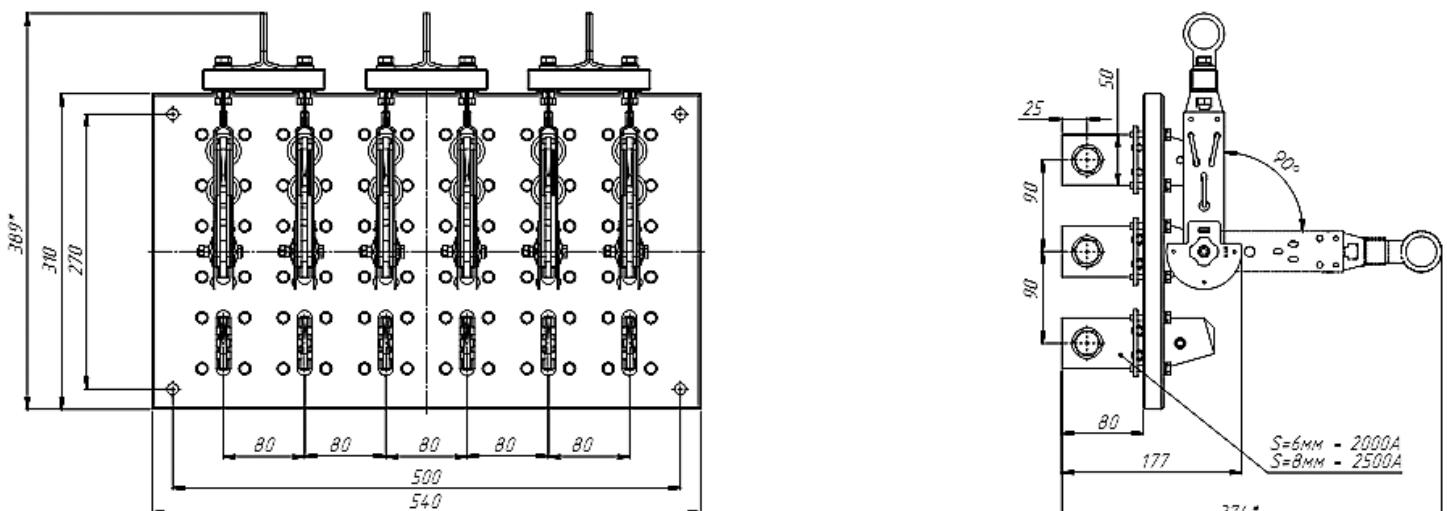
Разъединитель РЕ19 с боковой смещенной рукояткой РЕ19-44(45; 46)-31150-00 УХЛЗ
